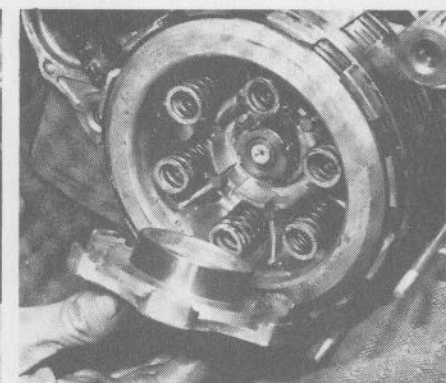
KOPPELING EN EINDAANDRIJFAS UIT HET BLOK
